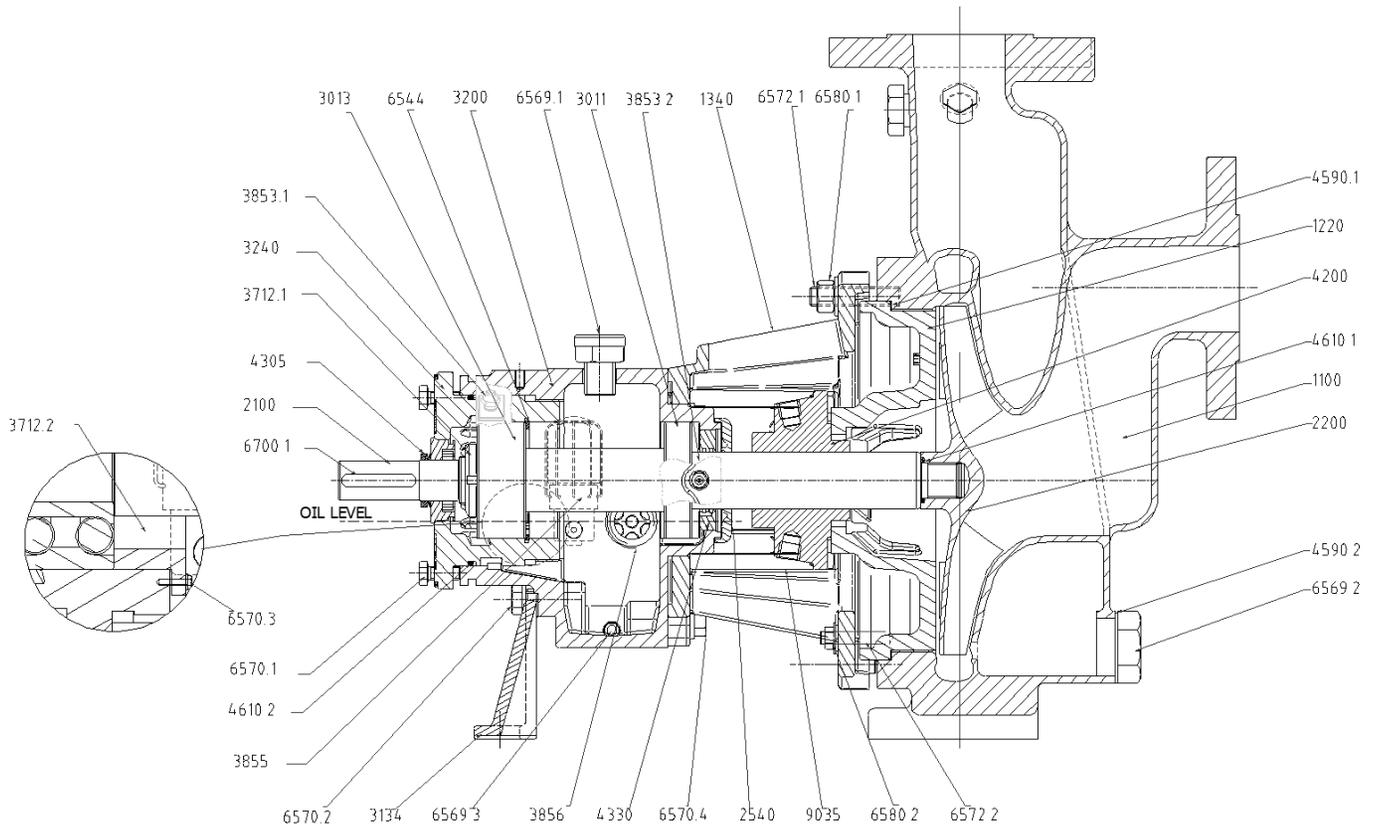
Plan en coupe de la pompe à auto-amorçage
